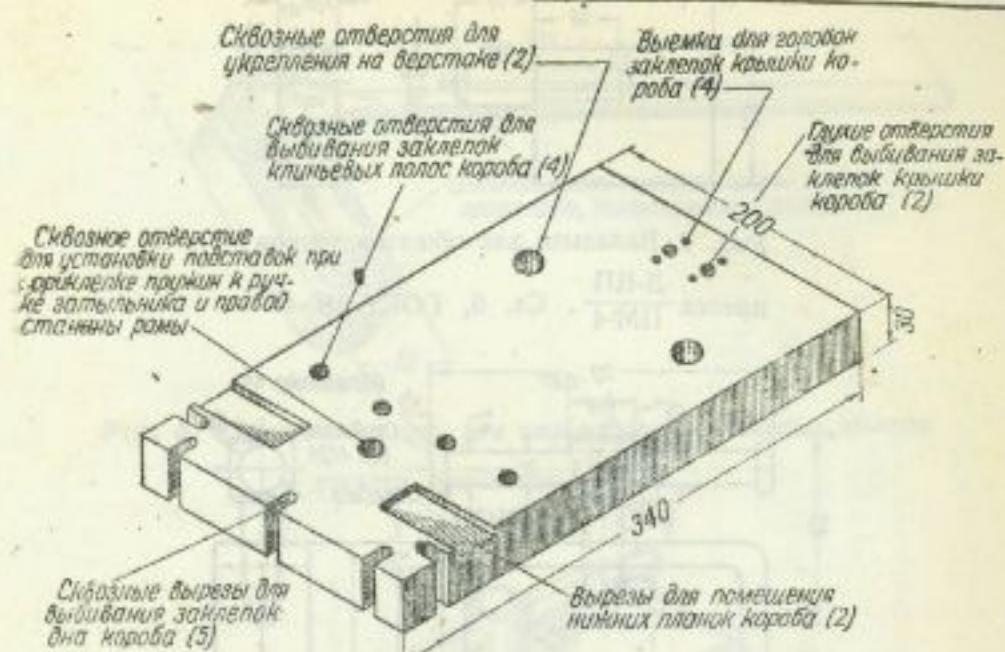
Подставка-наковальня для расклёпки заклёпок короба Д-ПП ПМ-1.
